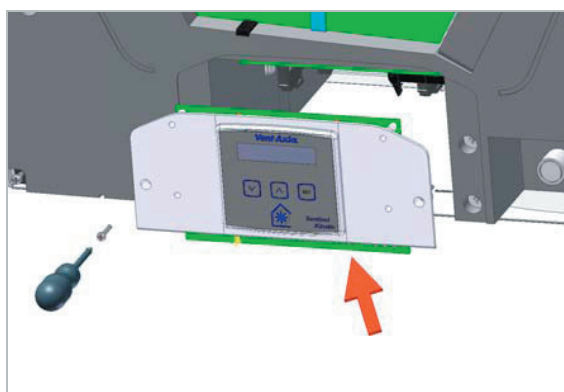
Odmontování krytu elektrického panelu (přední strana)
